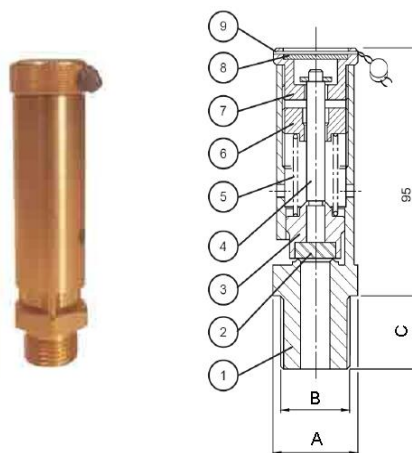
Клапан предохранительный: 1 - корпус; 2 - кольцо уплотнительное (нитрил); 3 – поршень; 4 – штанга; 5 - пружина; 6 – гайка регулировочная; 7 - крышка рифленая подъемного устройства; 8 – алюминиевая номерная табличка; 9 – проволока из нержавеющей стали и свинцовая пломба.
